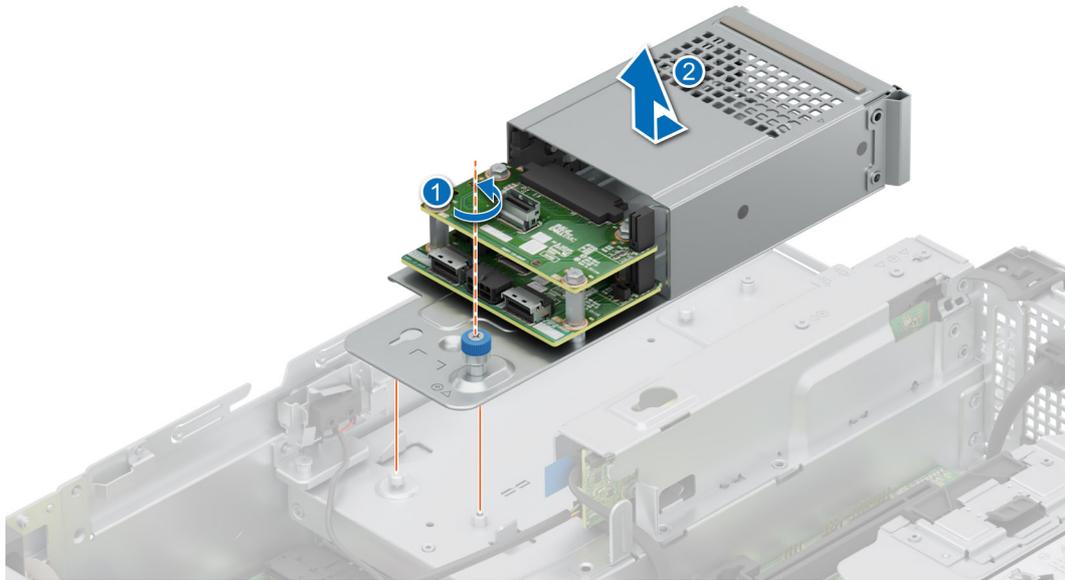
Entfernen des hinteren Laufwerksmoduls
